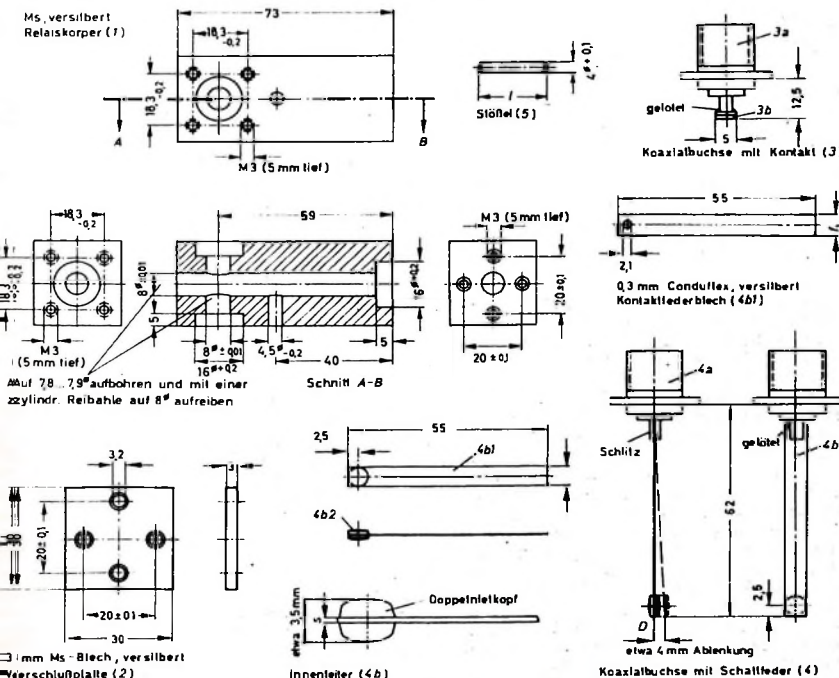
Einzelteile des Koaxialumschalters Ausführung A
